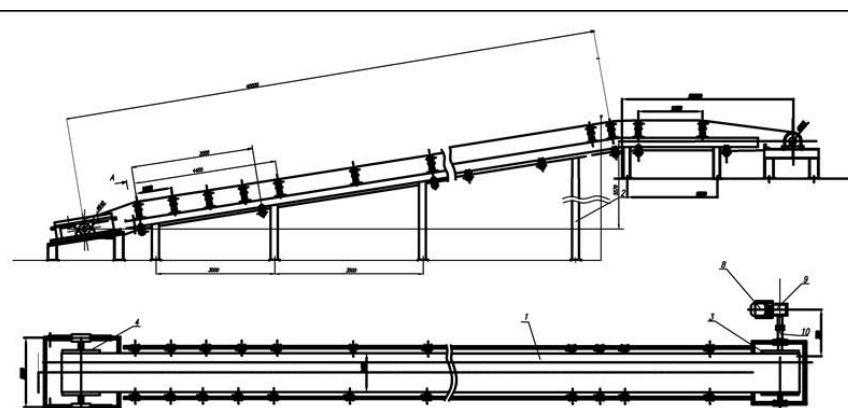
Конвейер ленточный реверсивный SMK-402
